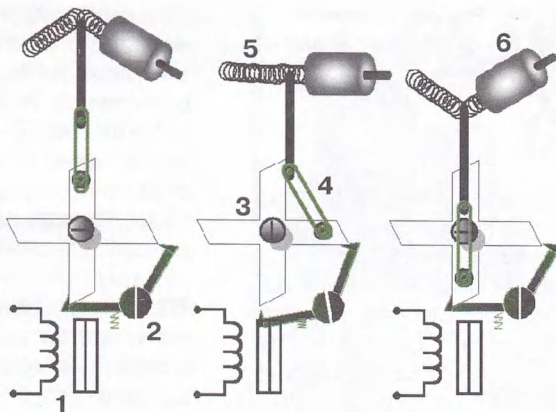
Схема управляющего устройства: 1 — реле; 2 — якорек; 3 — крестовина; 4 — рычажный механизм; 5 — пружина; 6 — электромотор.
